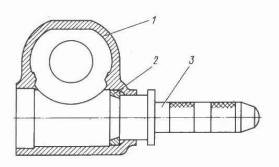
Desmontaje del aro exterior del cojinete superior del tornillo sinfín con ayuda del mandril 67.7853.9541:
